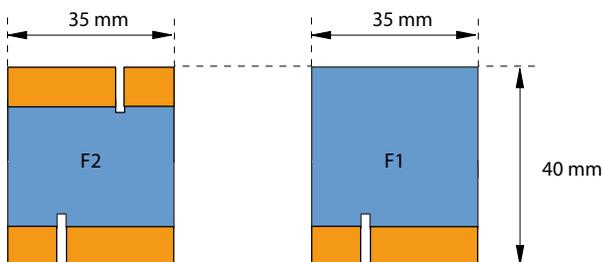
Dimensiones del adaptador de cableado (dibujo F)
